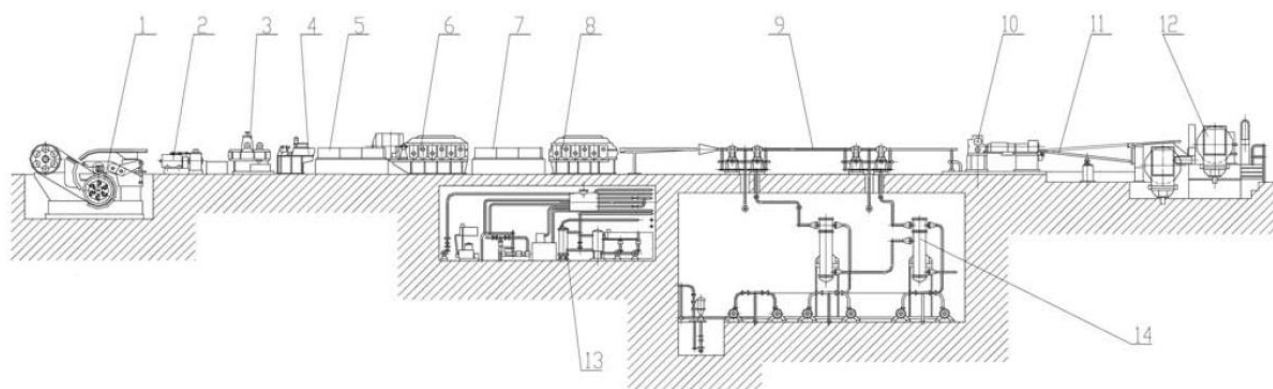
Схема агрегата литья и прокатки алюминиевой катанки:
